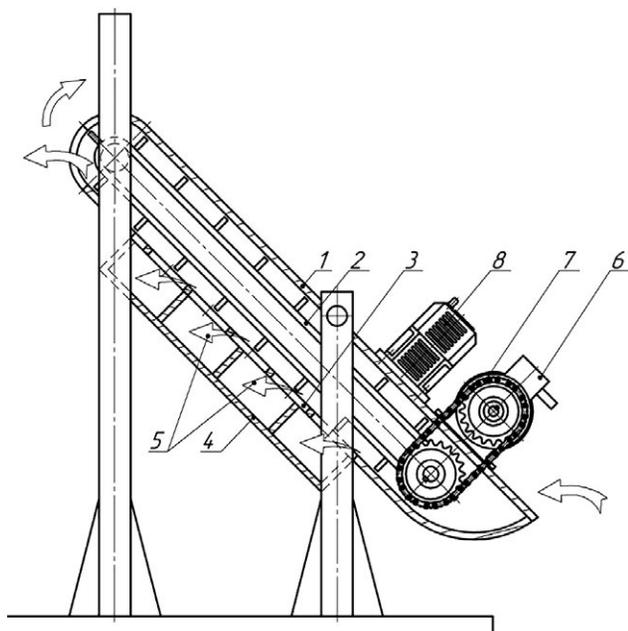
Принципиальная схема экспериментальной установки: 1 — корпус колосового элеватора; 2 — транспортёр скребковый; 3 — решётка; 4 — ёмкость; 5 — проход вороха; 6 — электродвигатель; 7 — передача цепная; 8 — частотный преобразователь «Веспер» E2-8300.
